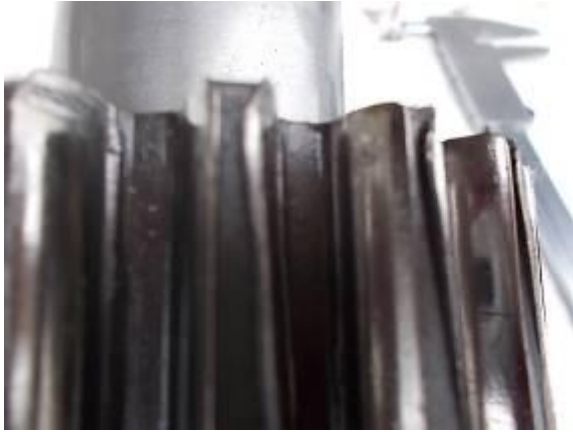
Zahnräder wo die Zähne weggedrückt wurden.
